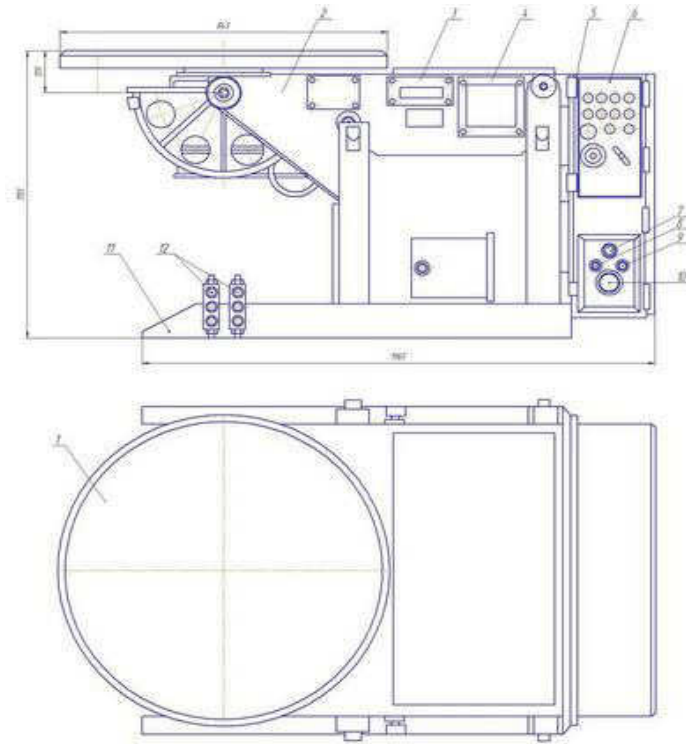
Манипулятор сварочный универсальный УСМ-1200
